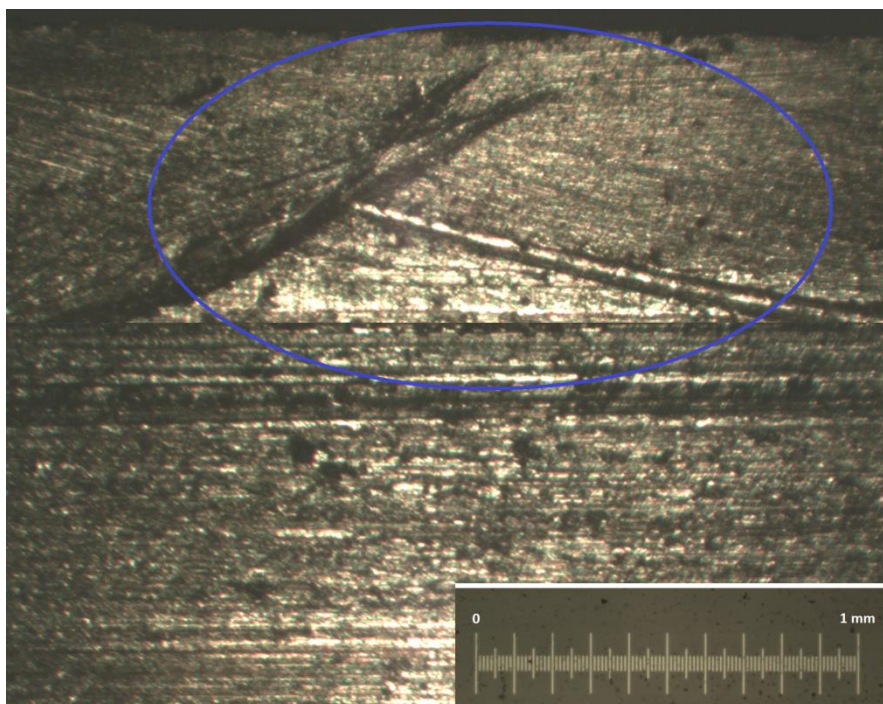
Superfície da bucha ensaiada com lubrificação de banho de óleo e rotação de 3400 rpm - detalhe da usinagem da borda ( Fonte: Autora)
